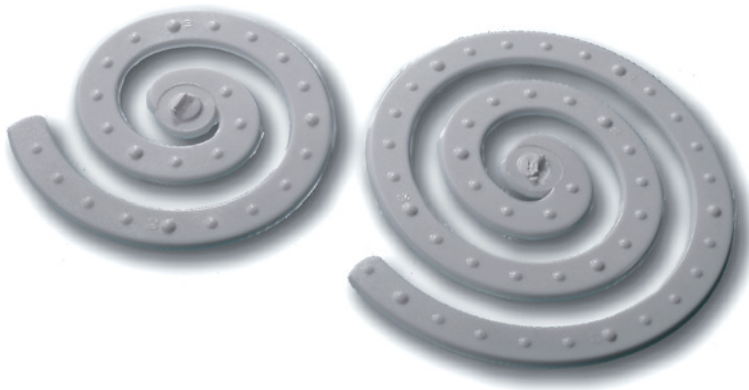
Fließspirale zur Messung der Fließweglänge
